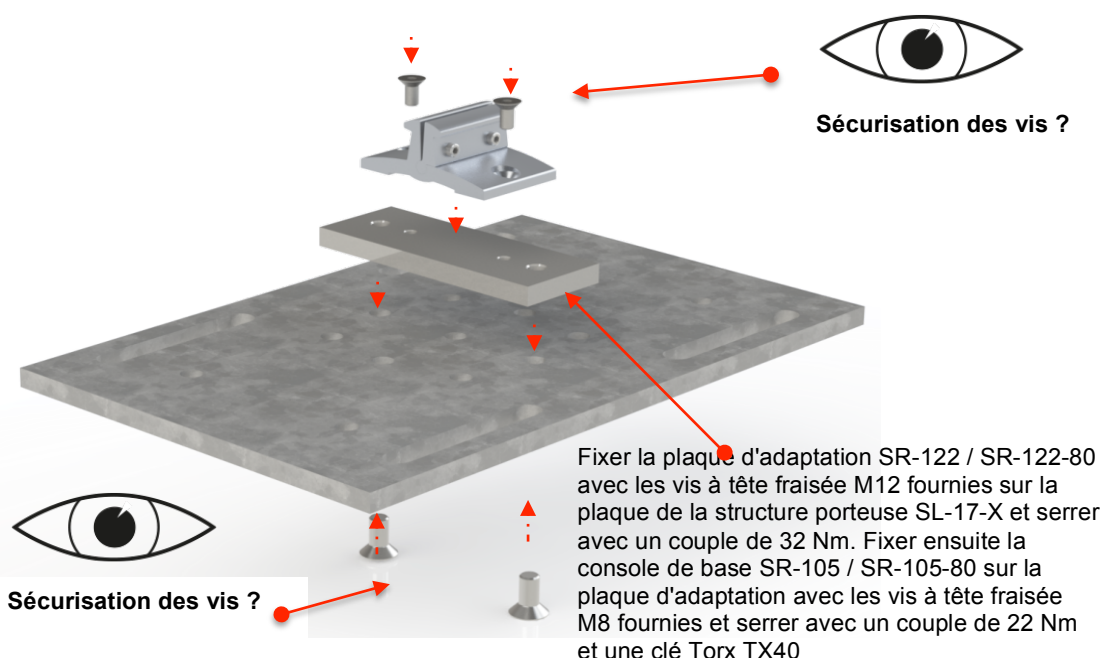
Montage de la console de base SR-105 sur la plaque d'adaptation SR-122 pour les plaques de structure porteuse SR-017
